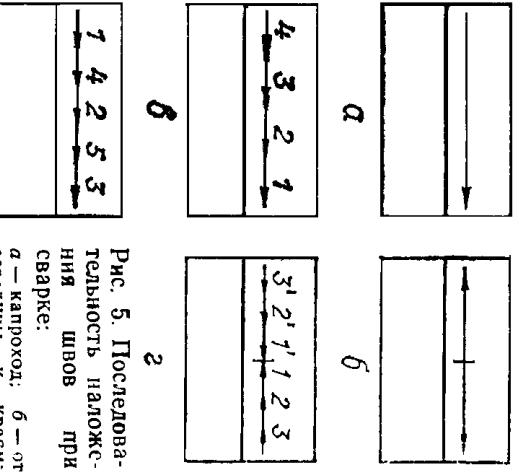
Последовательность наложения наплавки при сварке:
